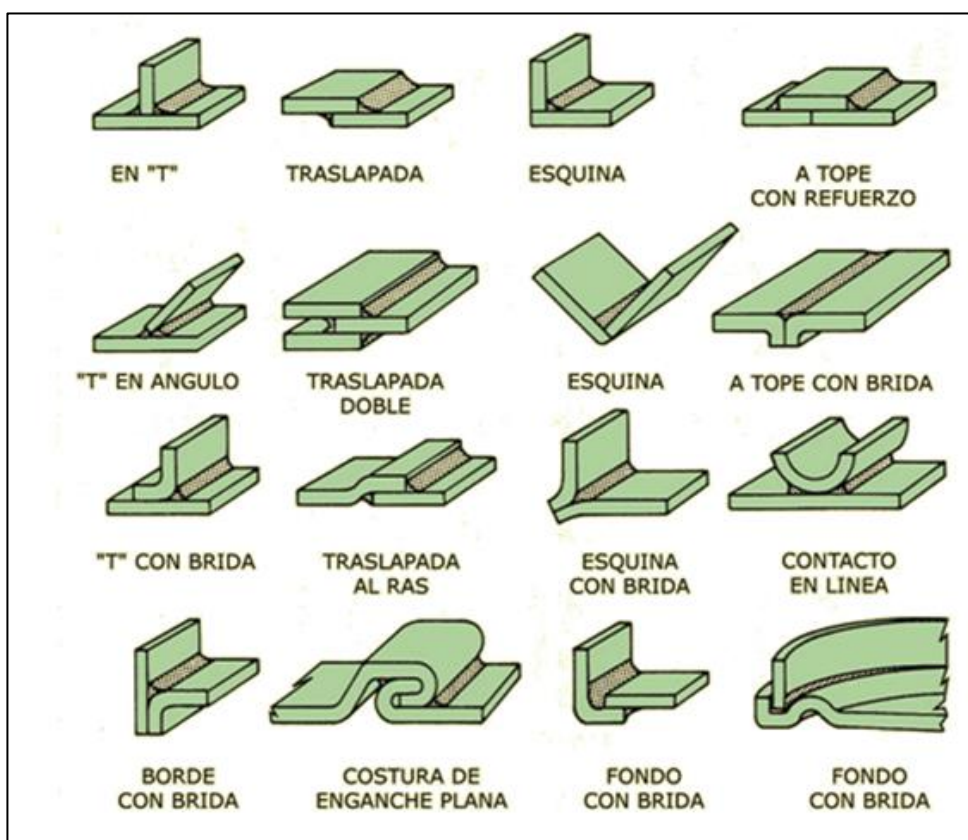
Diseño de uniones más habituales en soldadura. Fuente: web tecnología-técnica.
